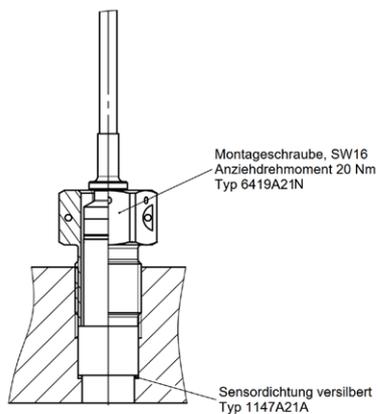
Montage mit Montageadapter Typ 6419A21N und Dichtung Typ 1147A21A
